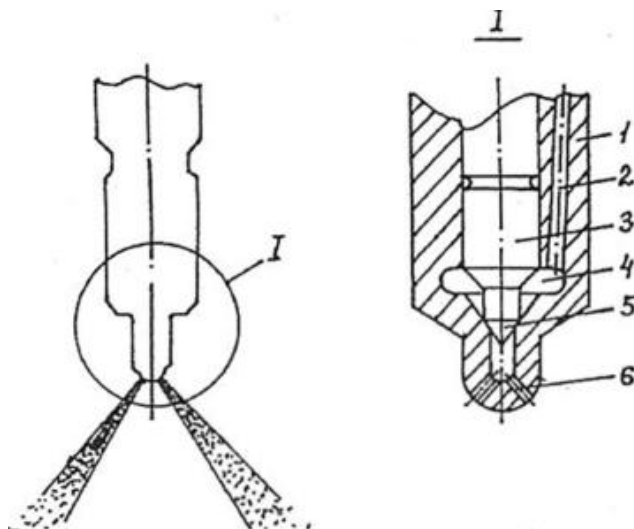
Распылитель струйной форсунки: 1 - корпус форсунки, 2 - топливный канал, 3 - подвижный шток, 4 - топливный коллектор, 5 - игла запорная, 6 - сопла распылительное.
